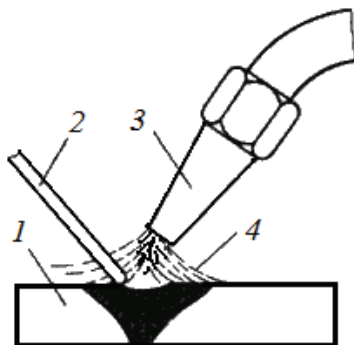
Схема газовой сварки: 1 — свариваемые заготовки; 2 — присадочный пруток; 3 — горелка; 4 — пламя
